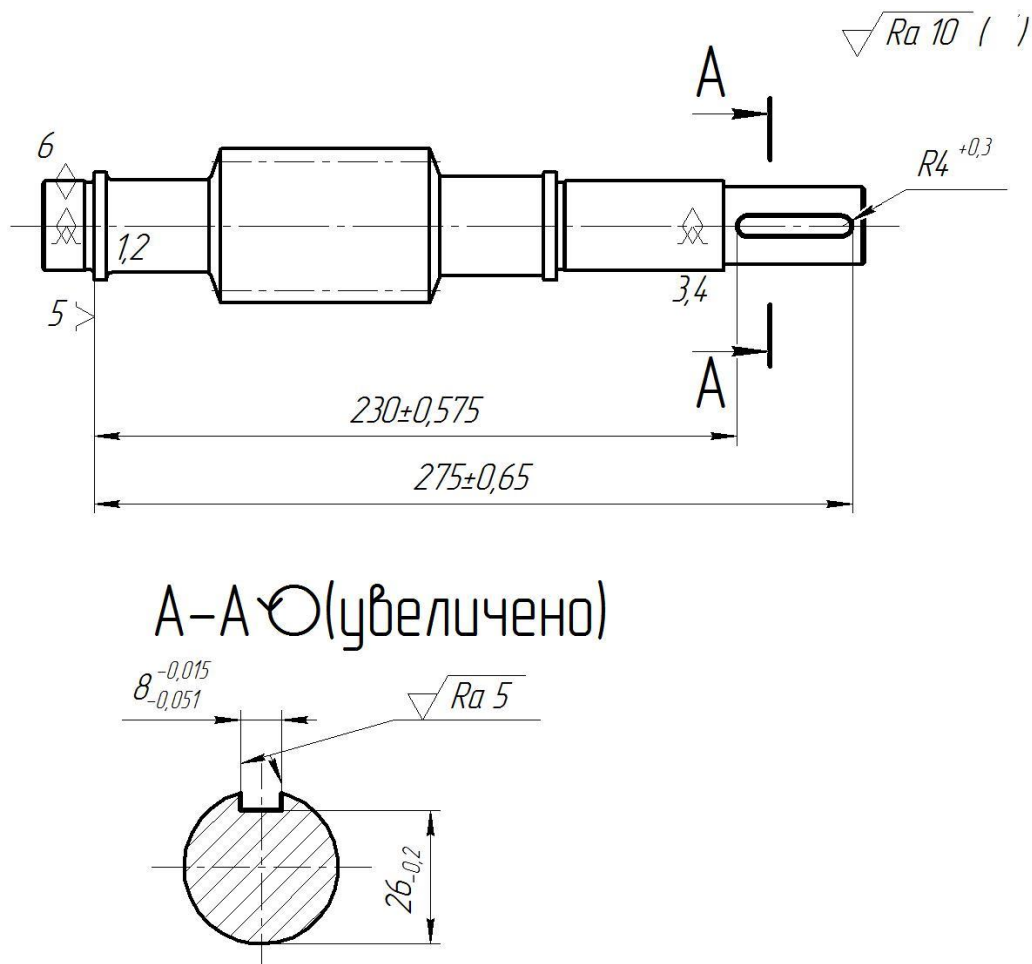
Эскиз шпоночно-фрезерной операции
